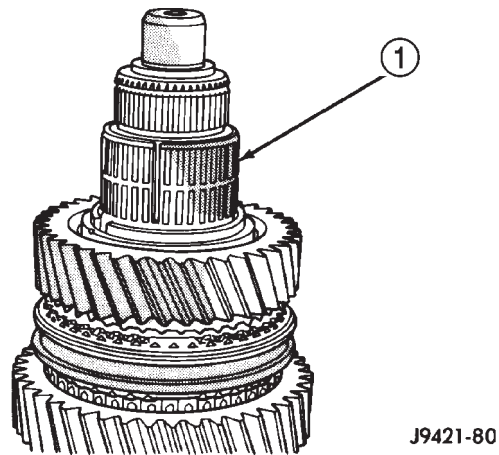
COJINETE DEL ENGRANAJE DE TERCERA
